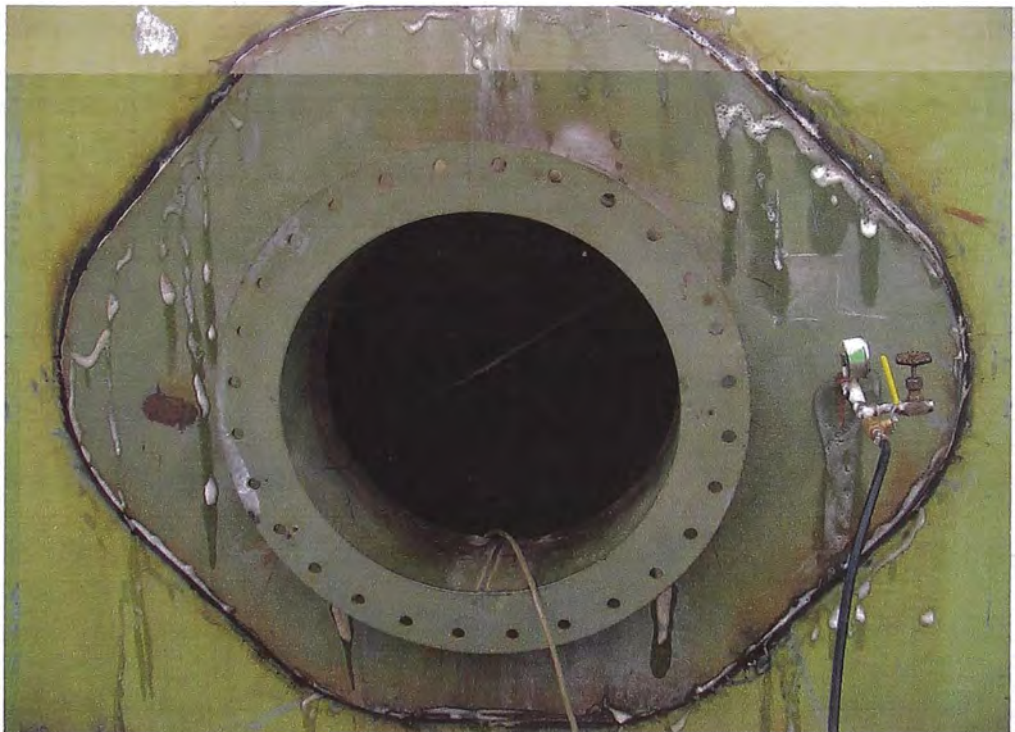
Prueba Neumática de las planchas de refuerzo de los manholes
